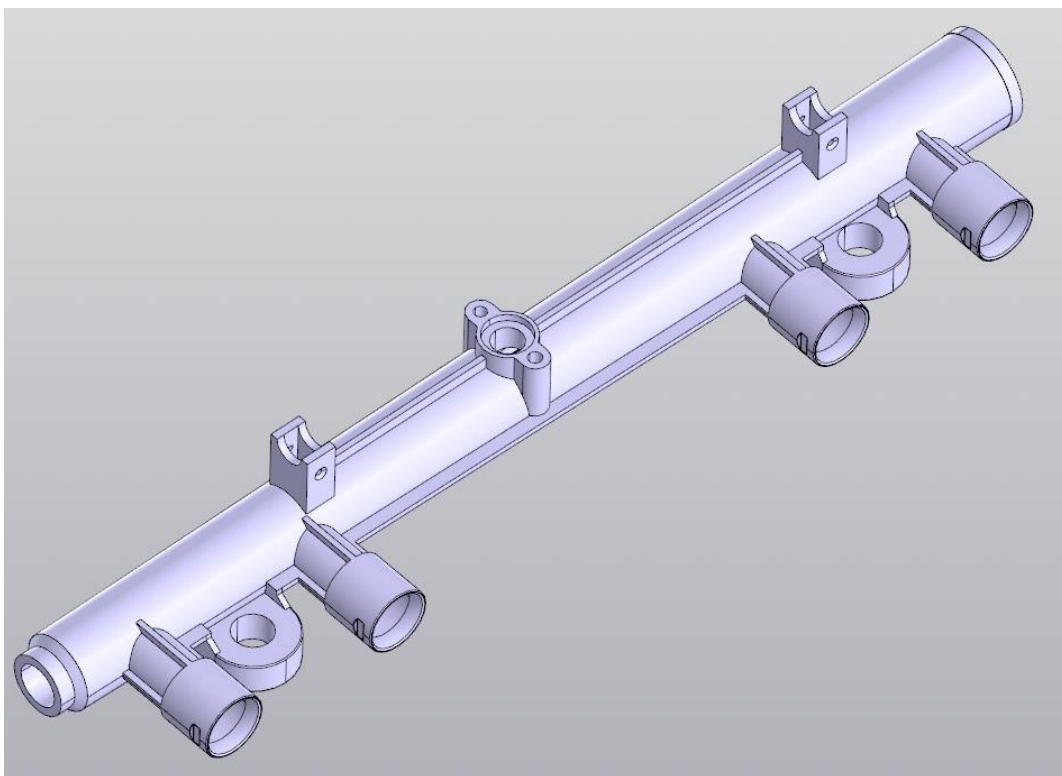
3D модель корпуса топливной рампы (вид снизу)
